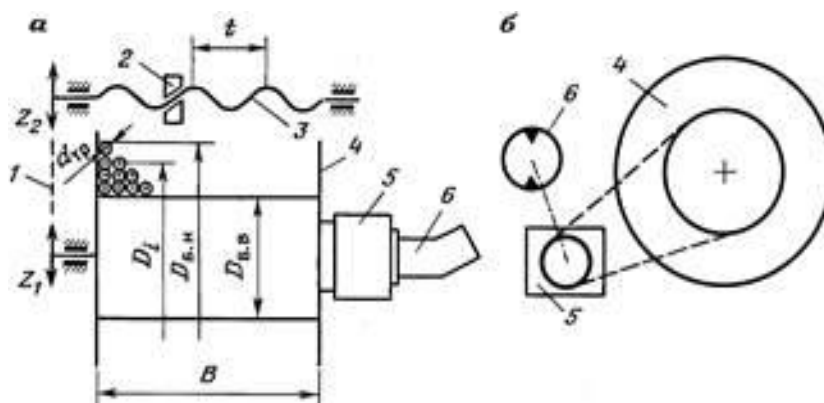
Кинематическая схема барабана для наматывания колонны гибких труб и их укладчика при использовании планетарного редуктора (а) и цепной передачи (б): 1 – цепная передача привода механизма укладки КГТ (Z_1, Z_2 – число зубьев звездочек); 2 – каретка; 3 – ходовой винт; 4 – катушка; 5 – планетарный редуктор; 6 – гидравлический мотор
